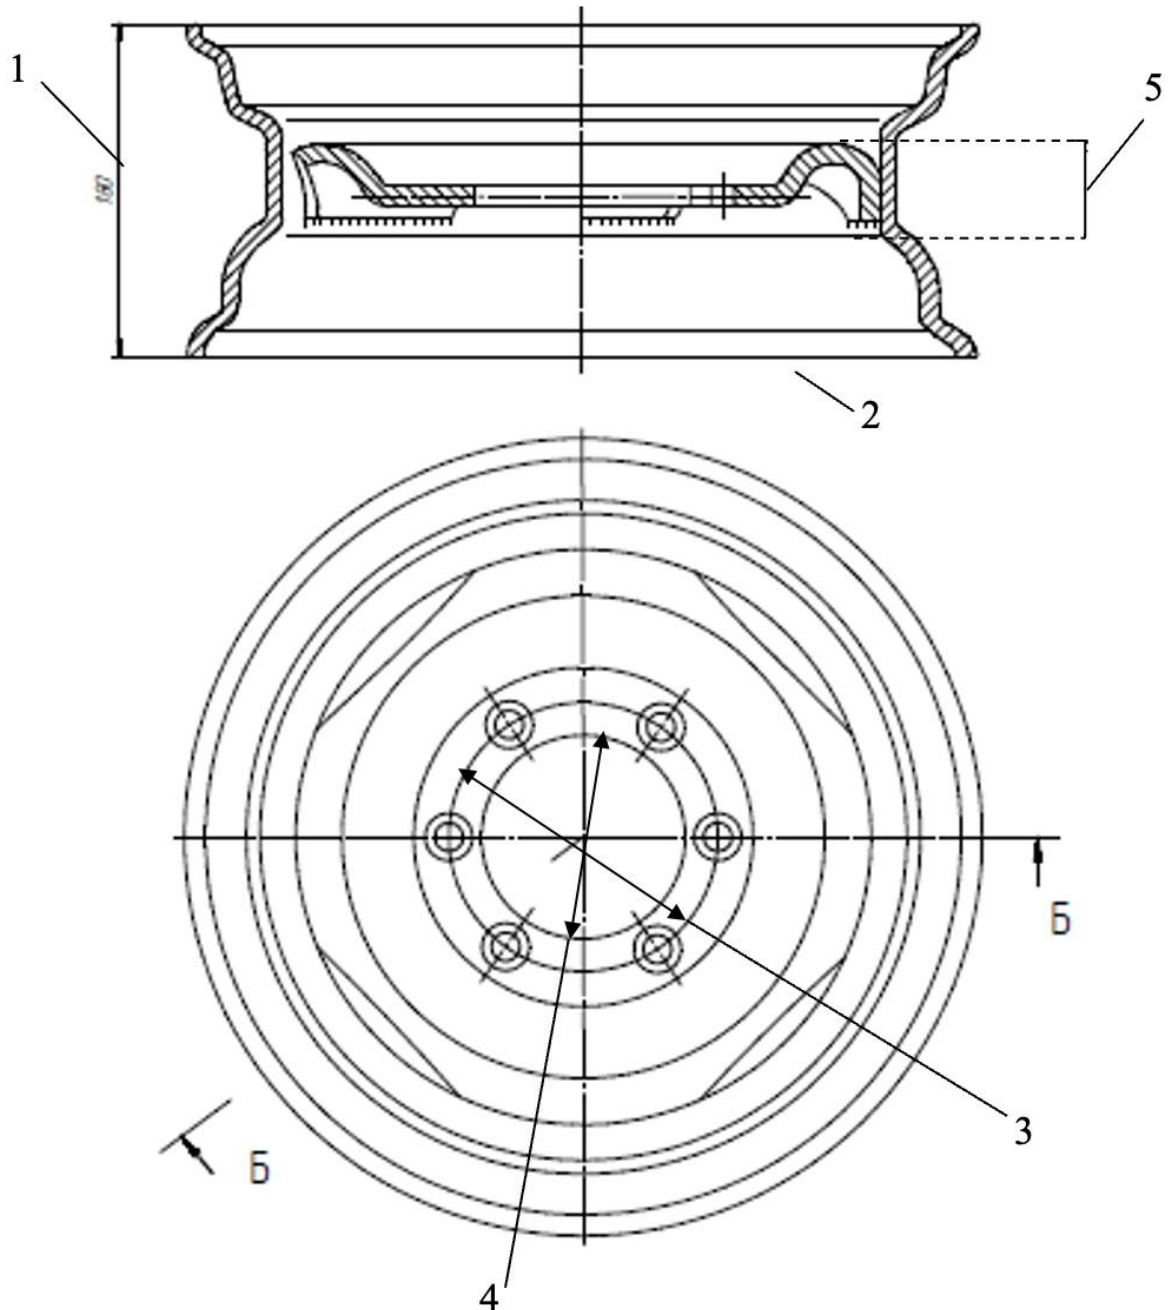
Схематичек зображення штамповано – зварного диска
